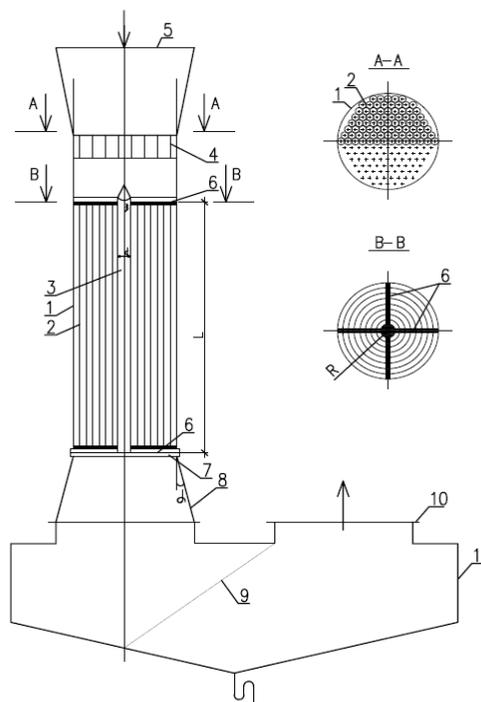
Коаксиальный сепаратор капельного аэрозоля: 1-сварной корпус, 2-адгезионно-осадительный элемент, 3-внутренний стержень, 4-стабилизирующее устройство, 5-конфузор для подвода очищаемого аэрозоля, 6-«гребенка», 7-опорная крестовина, 8-фланец диффузора, 9-стабилизирующая сетка, 10-патрубок отвода очищенного воздуха, 11-бункер для сбора и удаления коагулянта.
